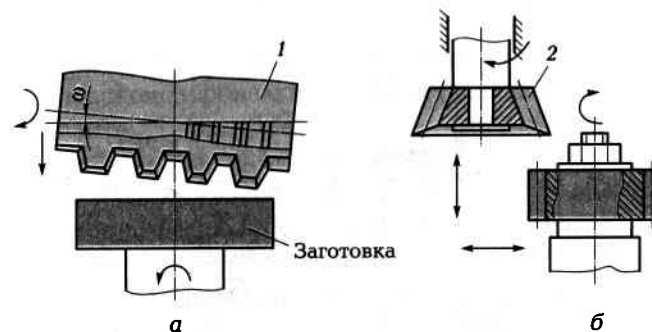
Схема нарезания зубчатых колес методом обкатки червячной фрезой на зубофрезерном станке (а) и долбяком на зубодолбежном станке (б)
